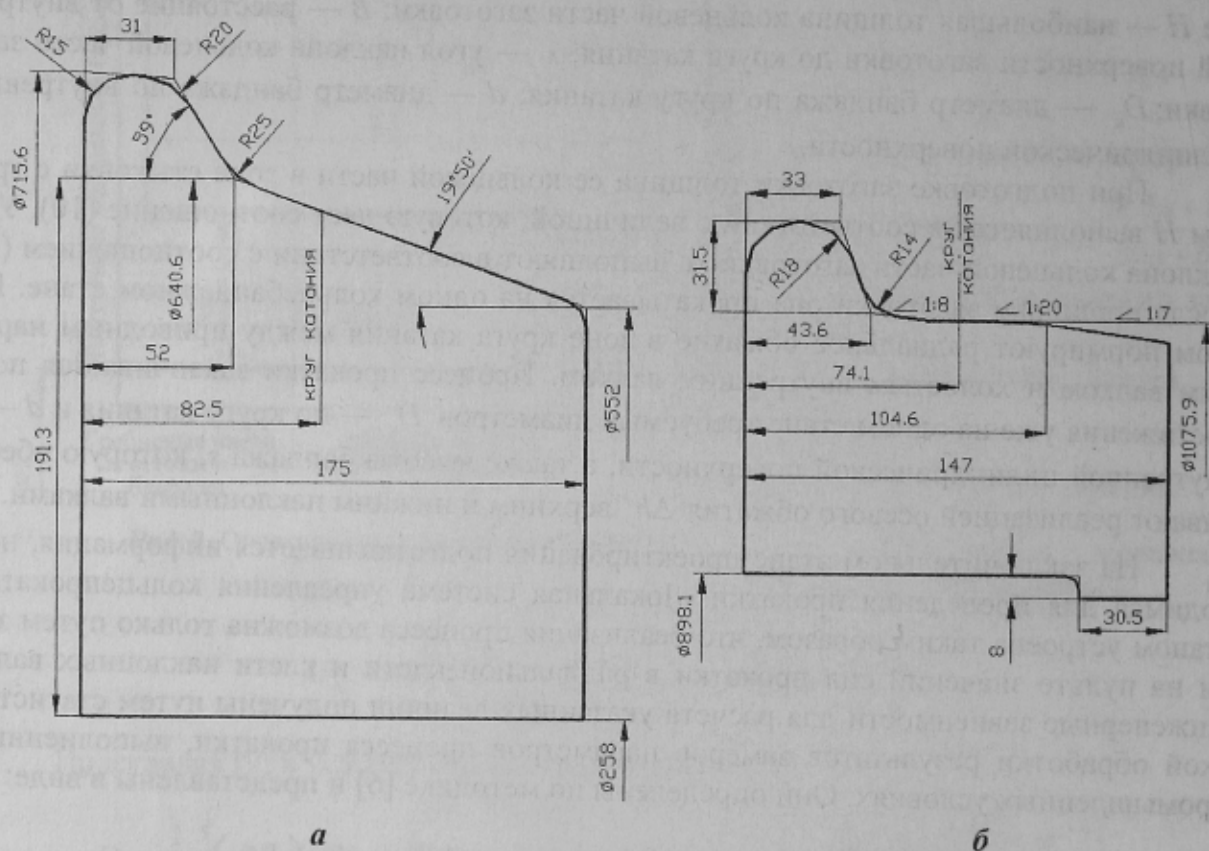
Профиль заготовки (а) и готового бандажа (б)  $\varnothing 890 \times 143$  мм
